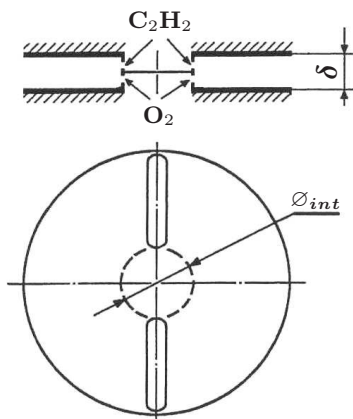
Vues en coupe et de face de la chambre de combustion centrifuge [17]
